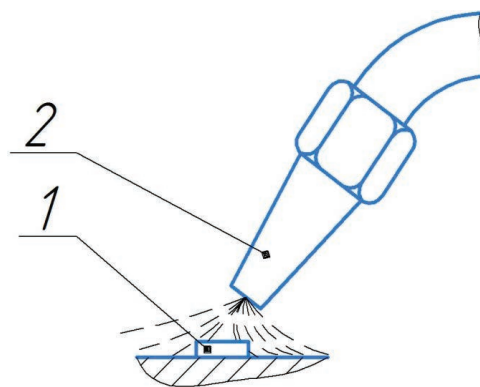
Нагрев сменной режущей твердосплавной пластины:
